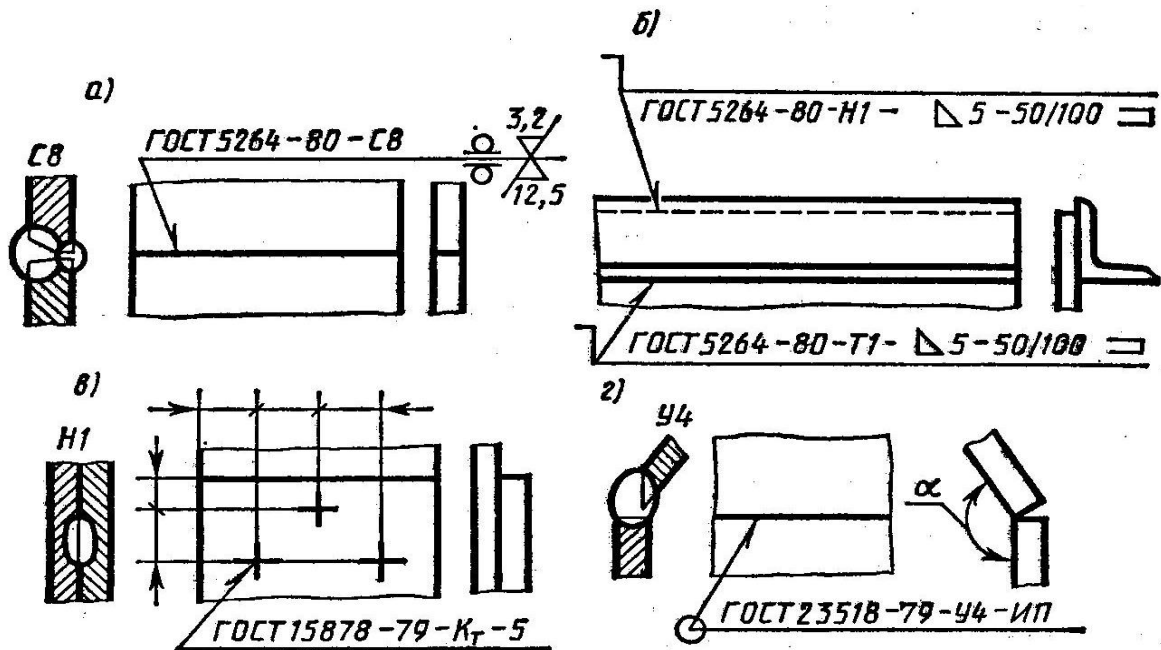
Примеры условного обозначения сварных соединений
